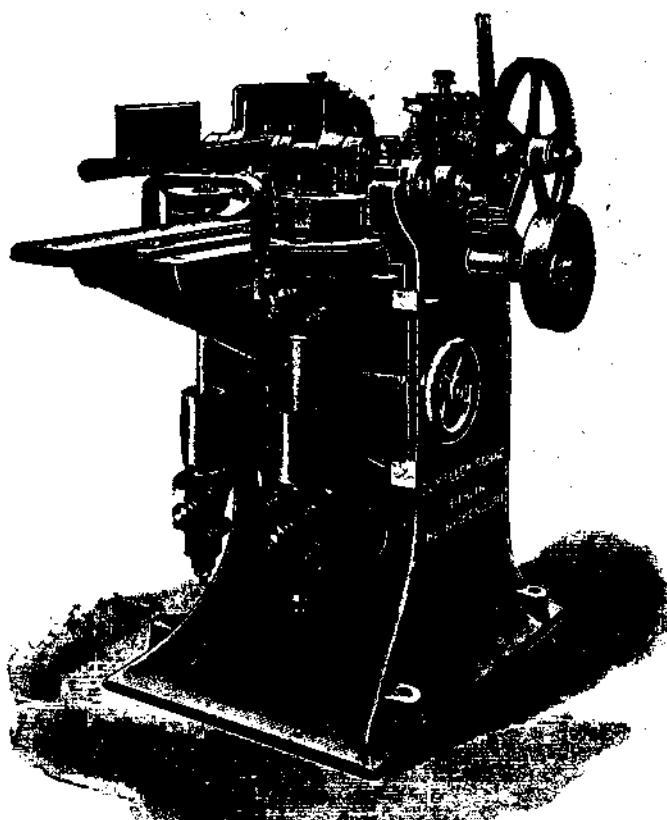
Строгальный станок для паркетных планок с тремя ножевыми валами.
